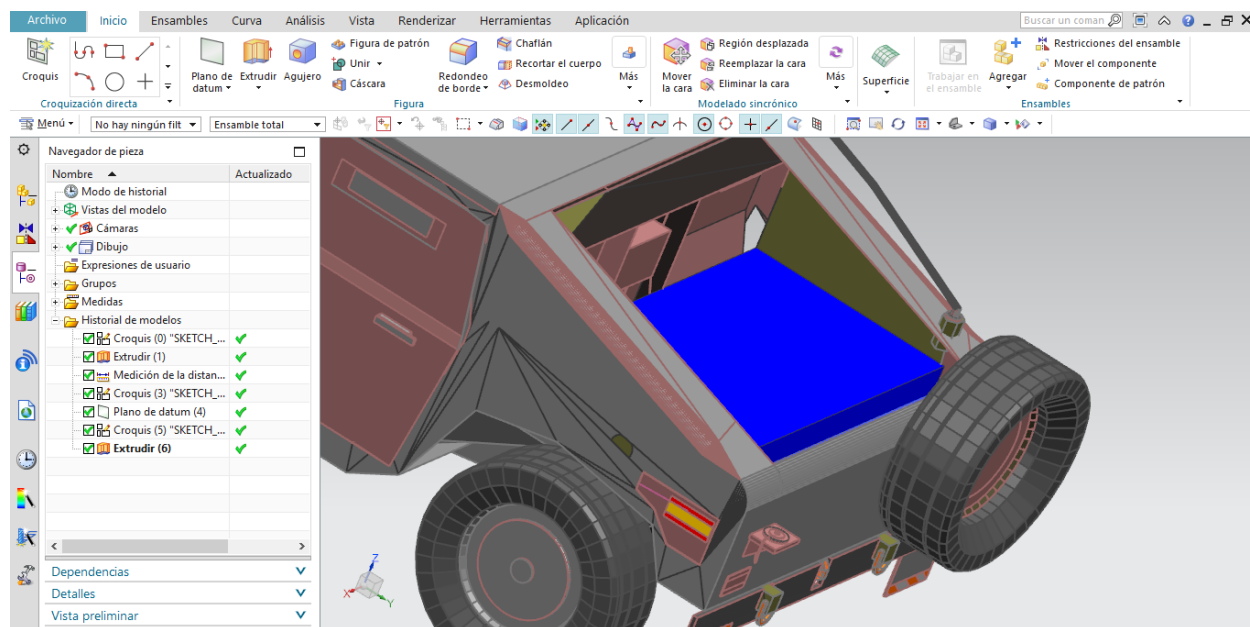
Espacio aprovechado en zona de carga para baterías
